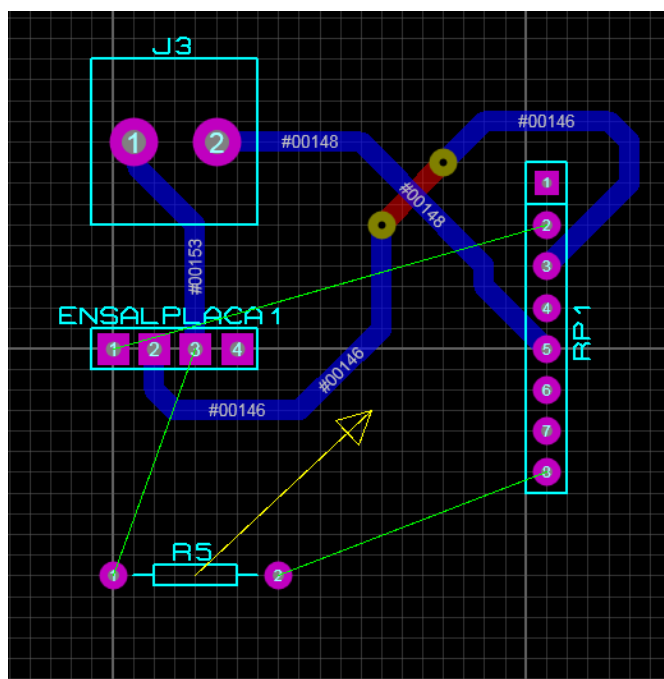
Enrutamiento manual de las pistas de la placa PCB
